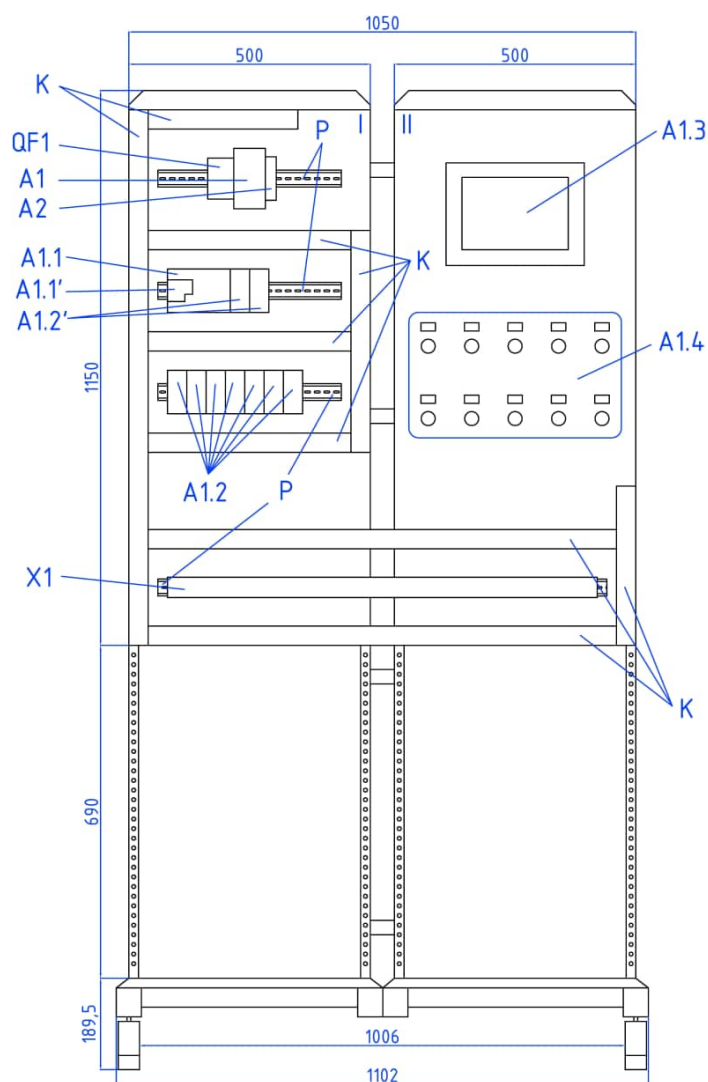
Эскизный чертеж лабораторного стенда:
